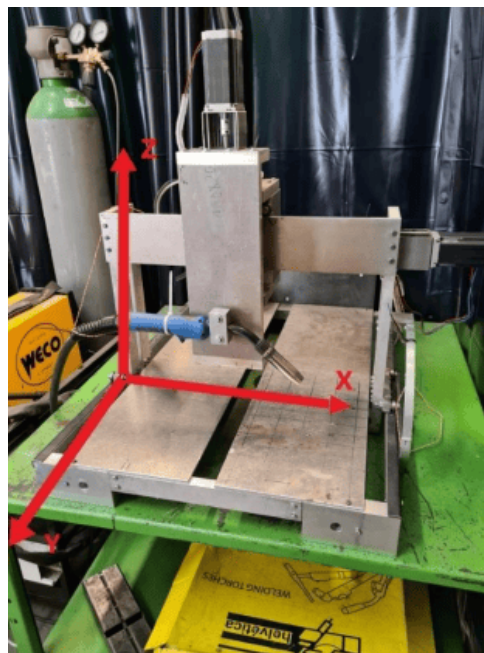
Mecanismo de soldadura com seus respectivos eixos [14].
